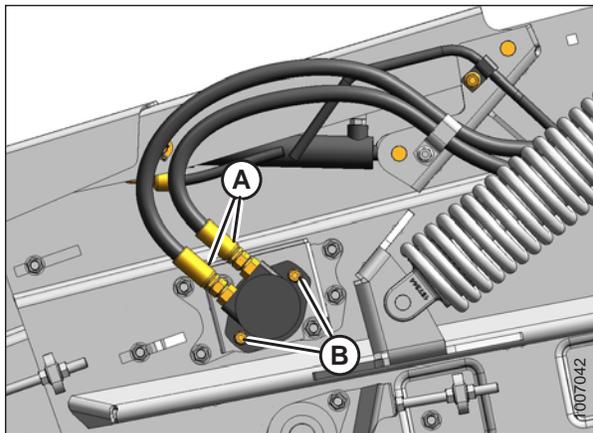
Motor hidráulico delantero; lado izquierdo
